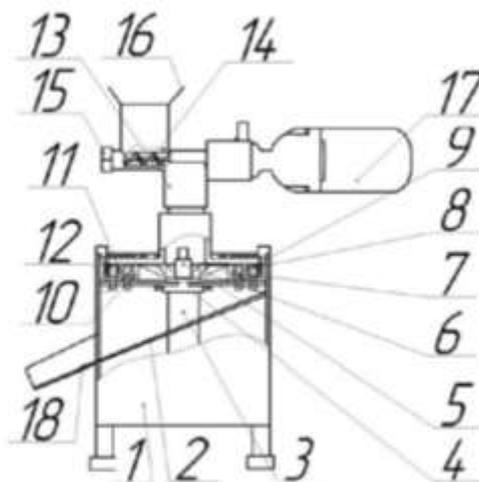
Принципиальная схема измельчителя зерна роторно-центробежного типа: 1 – корпус, 2 – наклонное днище, 3 – подшипниковый узел, 4 – вал приводной, 5 – ротор, 6 – гайка-отсекатель, 7 – распределитель, 8 – кольцевые выступы, 9 – кольцевые выступы, 10 – ножи, 11 – ножи, 12 – наружный ряд ножей, 13 – корпус дозатора, 14 – шнек, 15 – заглушка, 16 – загрузочный бункер, 17 – электродвигатель шнекового дозатора, 18 – выгрузное окно.
